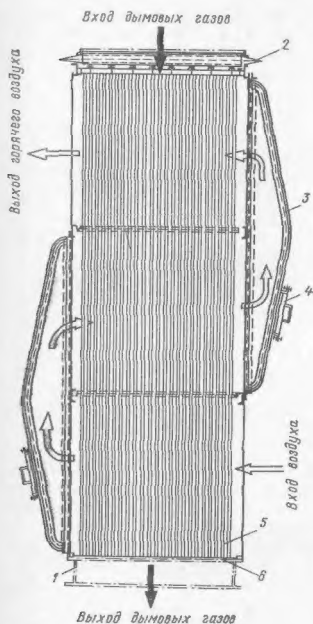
Однопоточный трехходовой трубчатый воздухоподогреватель
